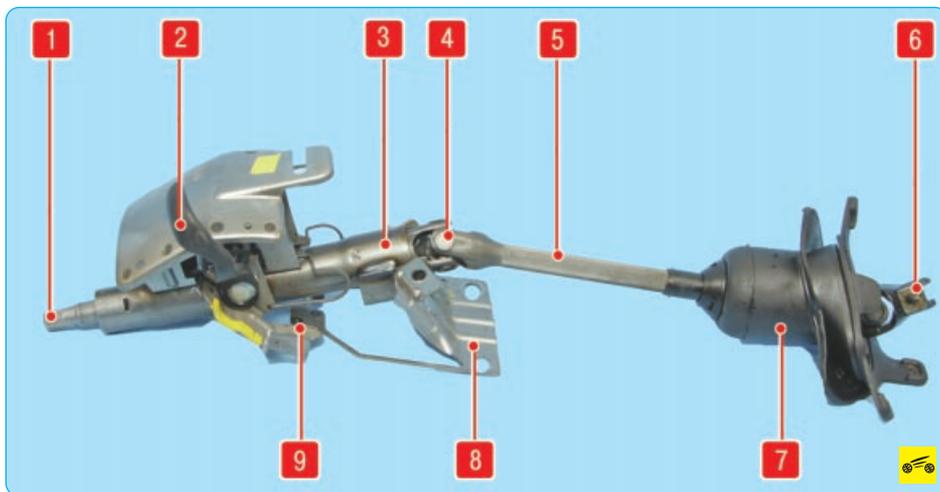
Рулевая колонка: 1 – рулевой вал; 2 – рычаг регулировки положения рулевой колонки; 3 – рулевая колонка; 4 – верхний карданный шарнир промежуточного вала; 5 – промежуточный вал; 6 – нижний карданный шарнир промежуточного вала; 7 – уплотнитель промежуточного вала; 8 – кронштейн крепления рулевой колонки; 9 – механизм регулировки положения рулевой колонки
